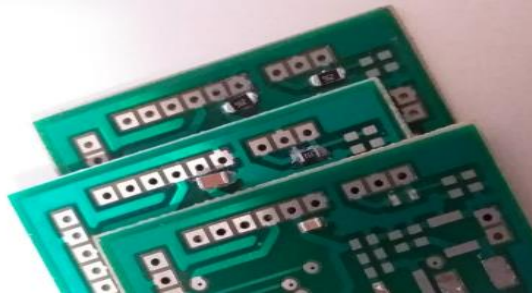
Placas con sus componentes SMD soldadas de manera correcta.
